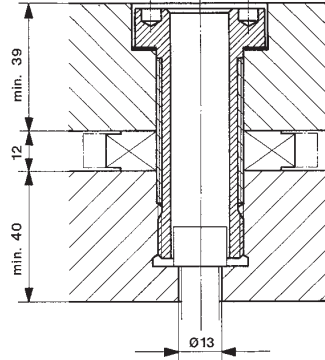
Vorspannung mit Hohldehnschraube Typ 9459. Bei dieser Variante besteht die Möglichkeit, die Grundplatte mit einer M12-Innensechskantschraube zentrisch zur Kraftaufnehmerachse durch die Hohldehnschraube hindurch zu befestigen. Siehe Datenblatt 7.9459.
